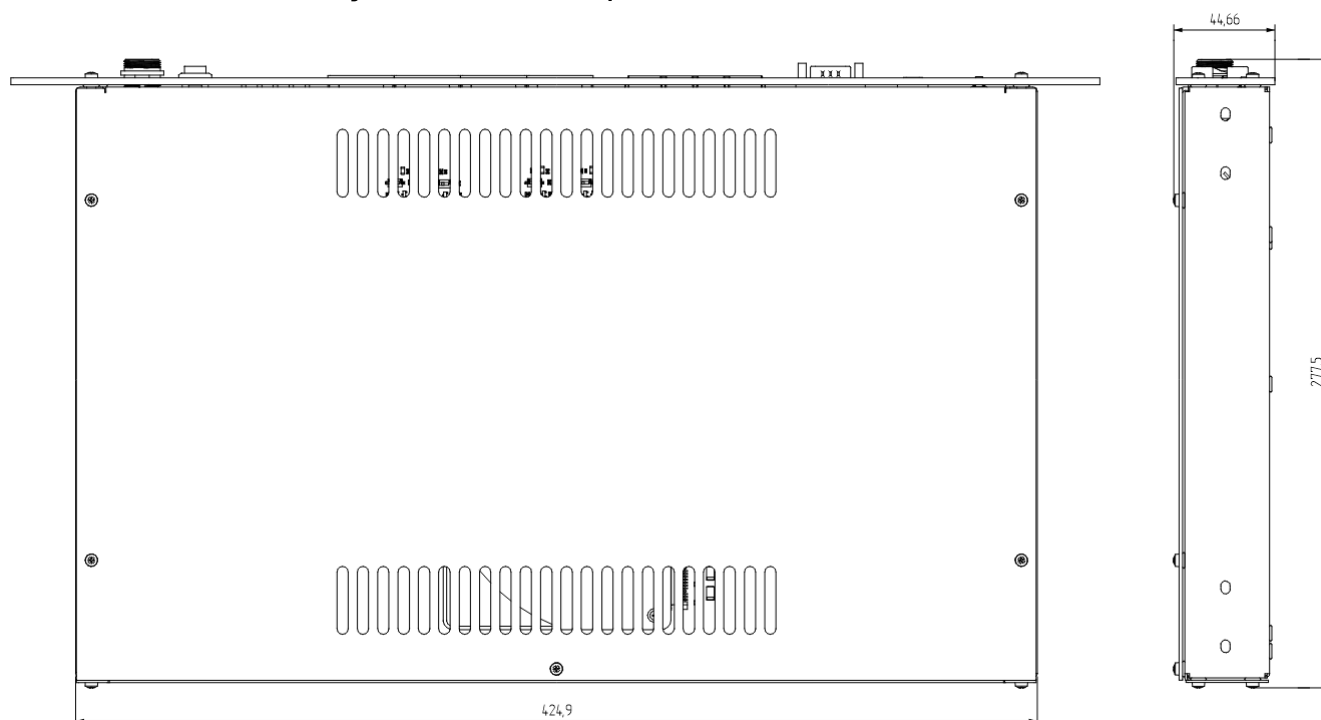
Размеры Изделия, вид сверху, вид сбоку
